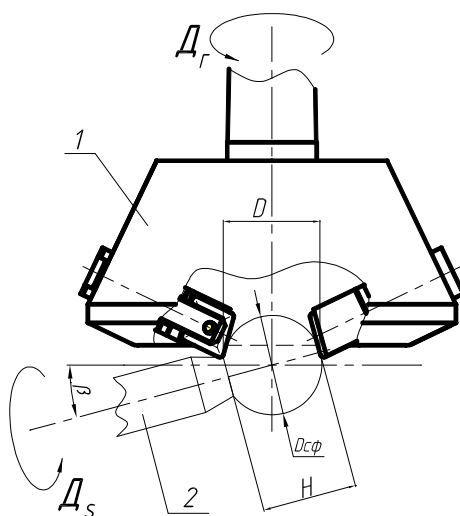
Схема охватывающего фрезерования сферической поверхности детали
